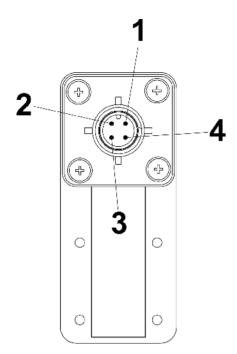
Pin-Belegung Gerätestecker M12x1 (Form 30x70)
